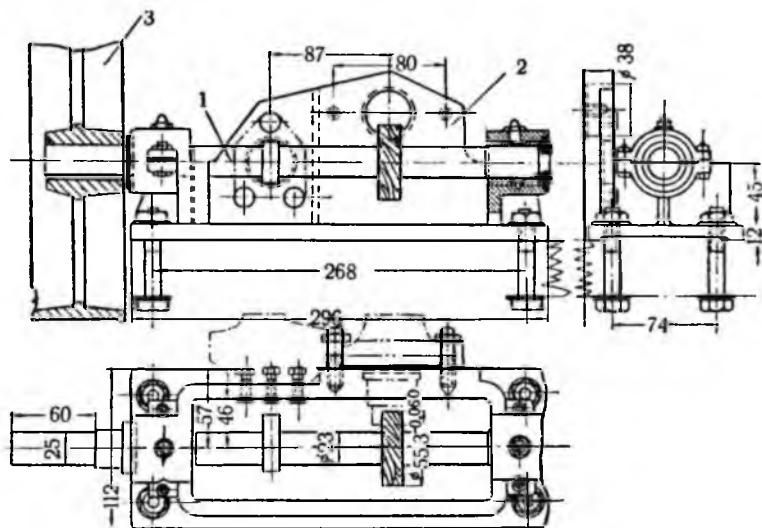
Установка подкачивающей помпы ЧТЗ или ККАЗ на испытание на добавочном приводе стенда ТА-5-ВИМЭ:
